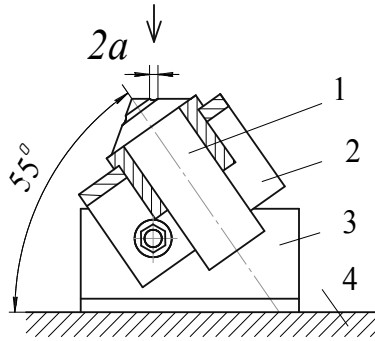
Пристрій для вимірювання ширини канавки зноса
